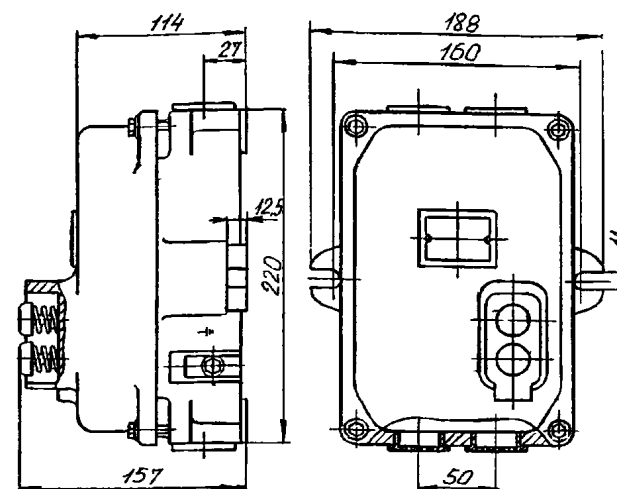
Габаритные и установочные размеры выключателя в металлической оболочке (масса до 3,5 кг)
